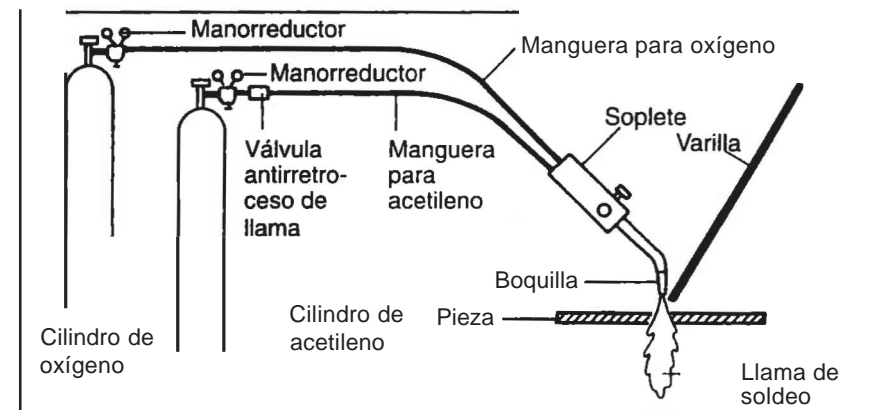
EQUIPO DE SOLDEO OXIACETILÉNICO
